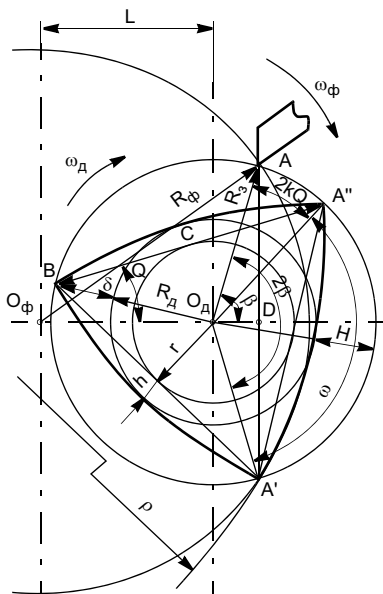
Схема попутного фрезоточения некруглого профиля с внутренним касанием детали и фрезы
